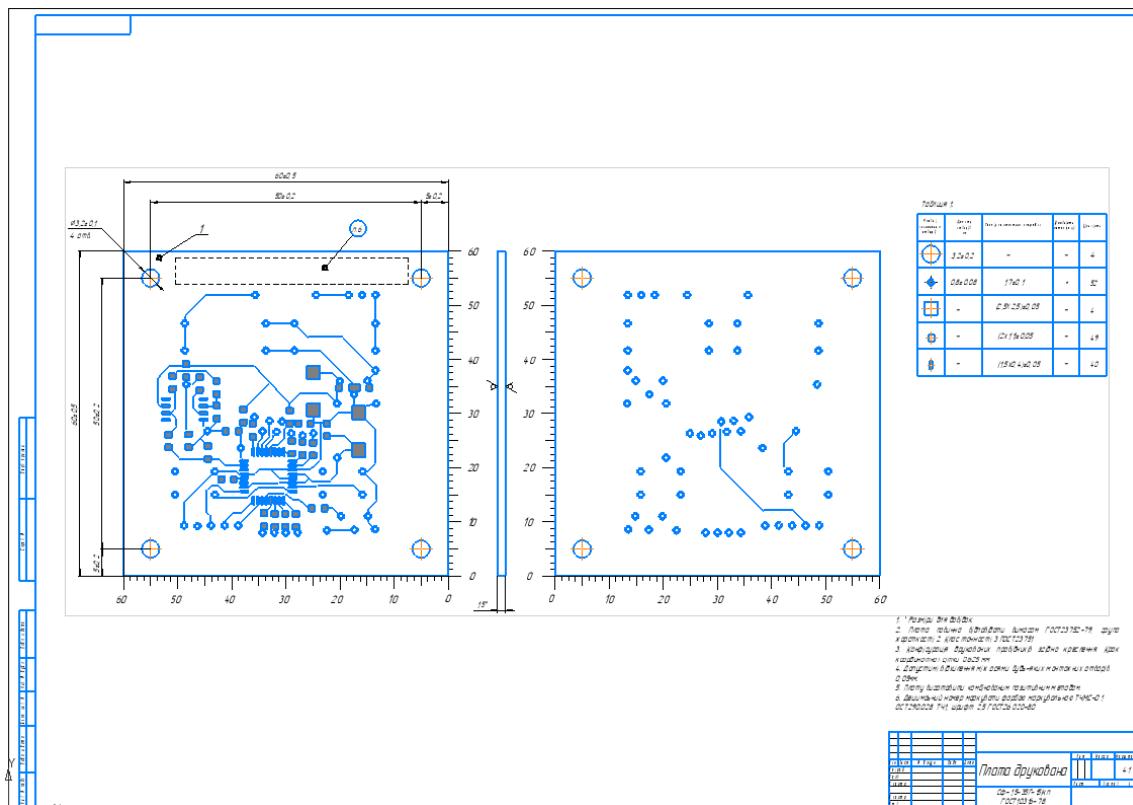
креслення друкованої плати мікроконтролерного блоку керування паяльною станцією
